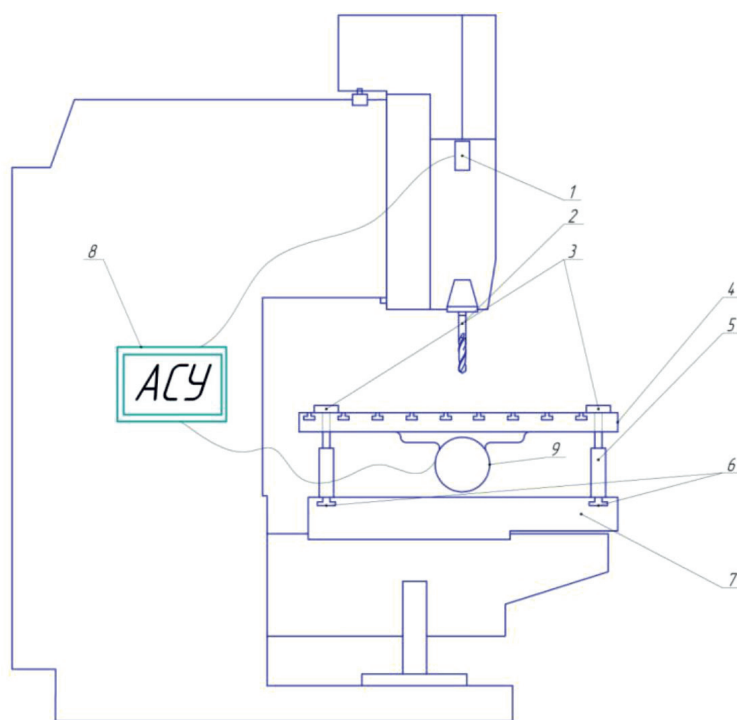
Схема вибропривода на фрезерном станке: 1 – датчик скорости шпинделя, 2 – инструмент, 3 – регулировочные болты, 4 – вибростол, 5 – втулки, 6 – крепежные болты, 7 – стол станка, 8 – автоматическая система управления, 9 – вибропривод
